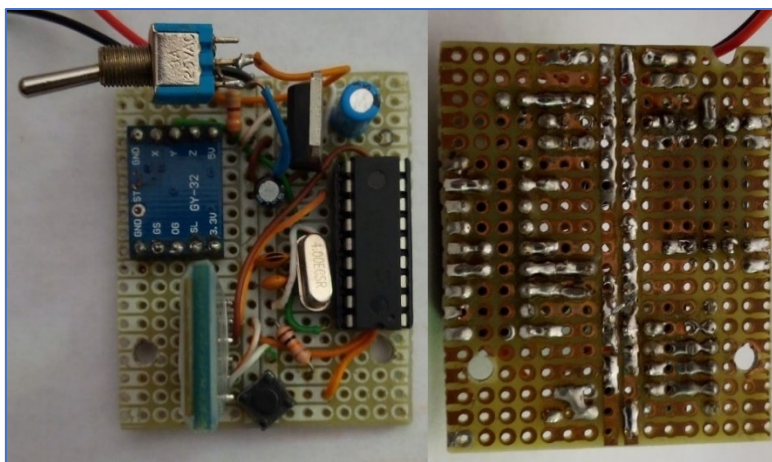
Circuito montado y soldado en placa fenólica perforada
